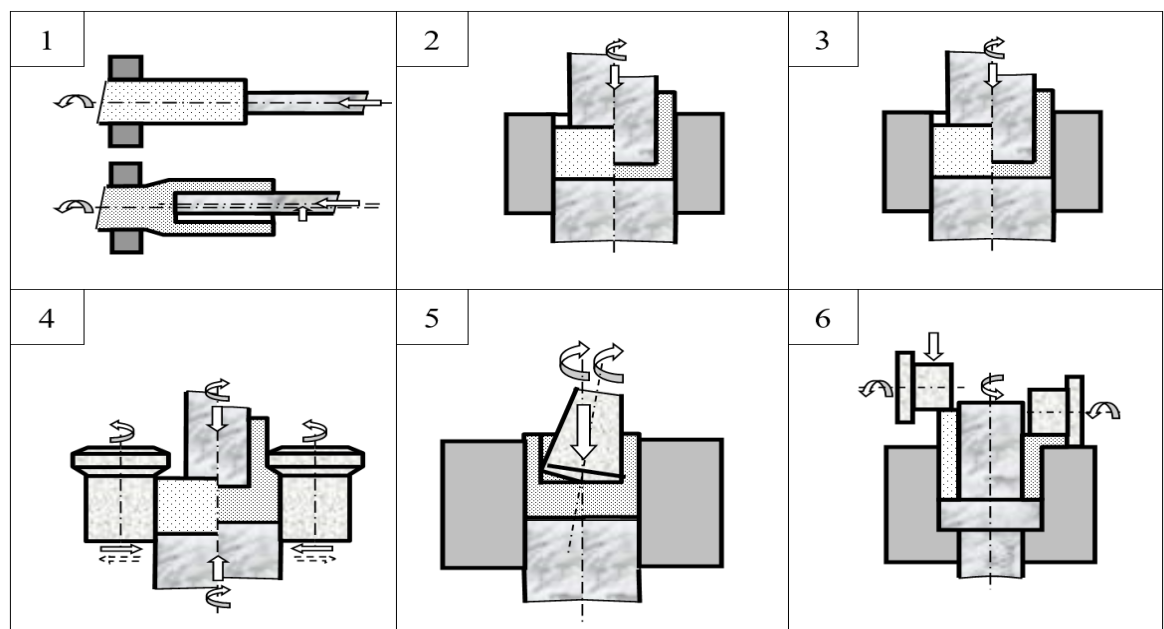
Способи виготовлення порожнистих деталей з різною кінематикою руху інструменту
